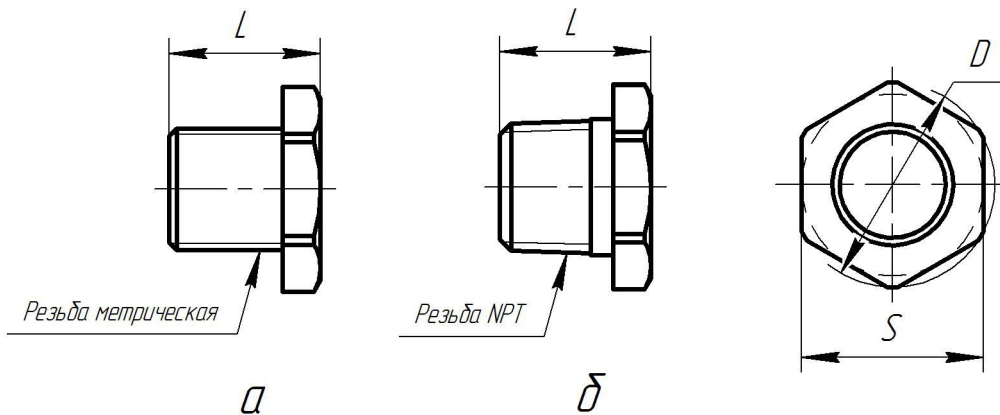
а - заблужки с метрической резьбой, б - заблужки с NPT резьбой
